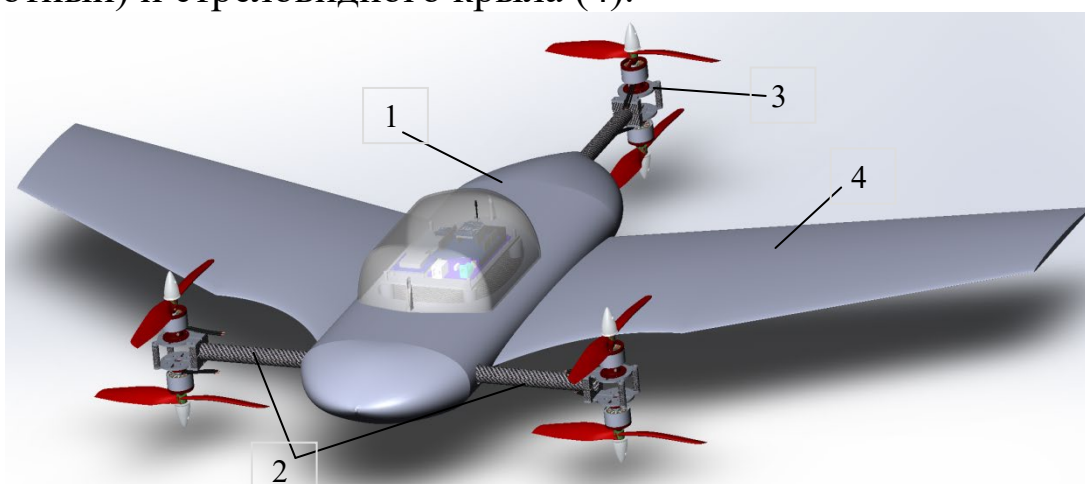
Общий вид БПЛА типа конвертоплана
